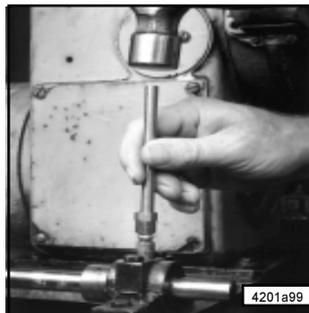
Montage des Zerk-Lock-Körpers mittels Treibwerkzeug
